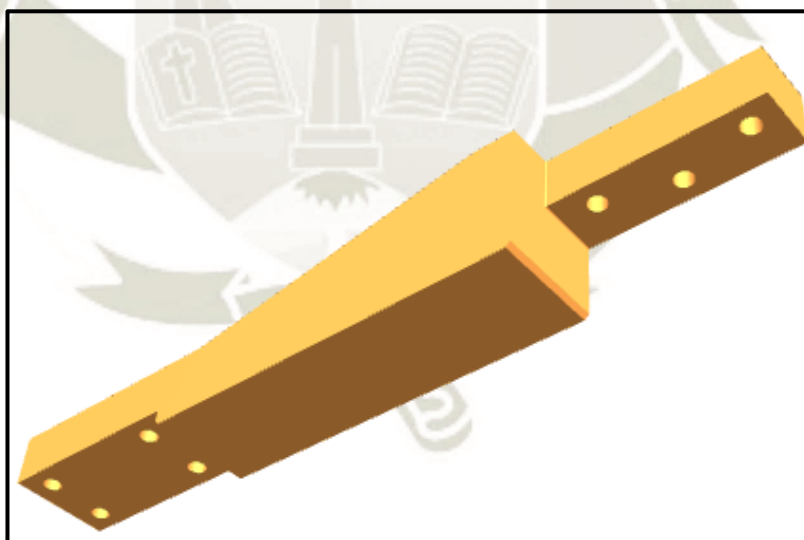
Diseño de placa de montaje original (*Mounting Plate*)
